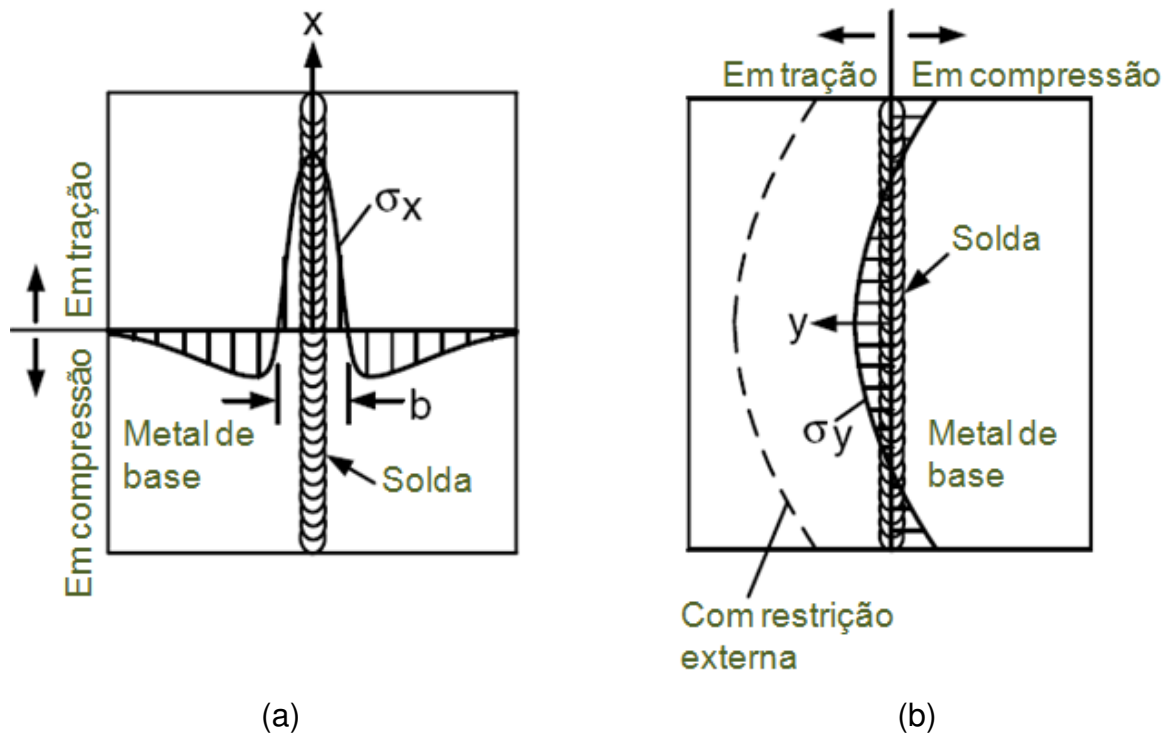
Distribuição das tensões residuais longitudinais (a) e transversais (b) em juntas de topo. Adaptado de Kou (2003).
